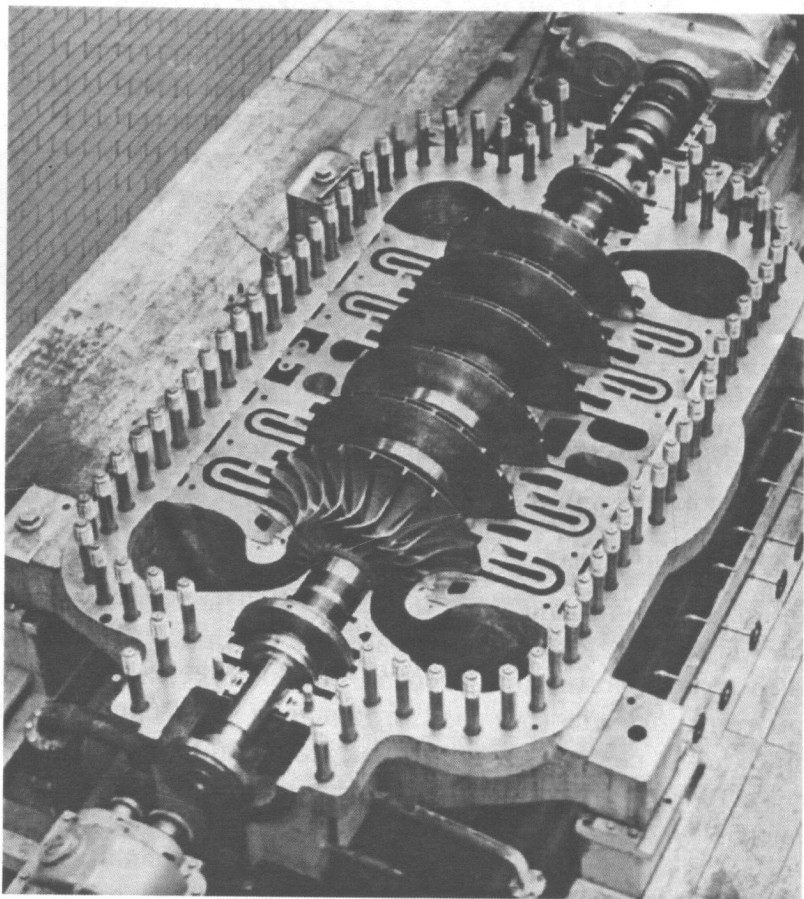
Загальний вигляд проточної частини відцентрового компресора з горизонтальним розніманням корпусу
